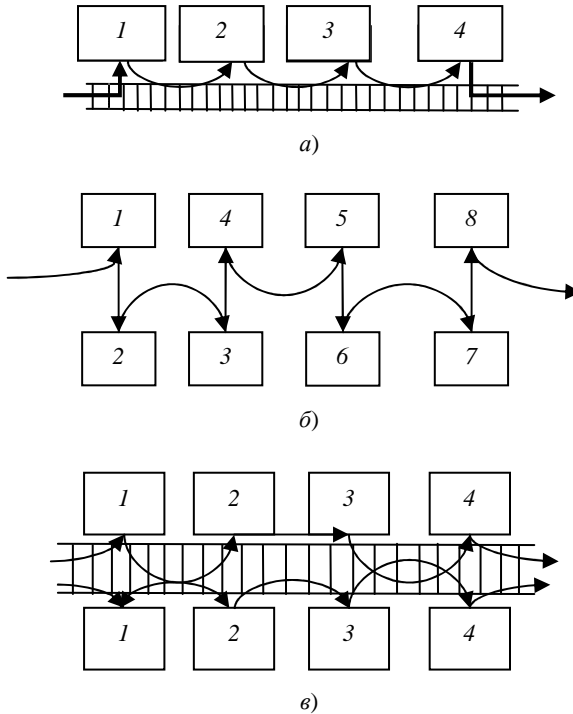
Расположение станков в поточной линии (цифры обозначают порядковый номер станка)
